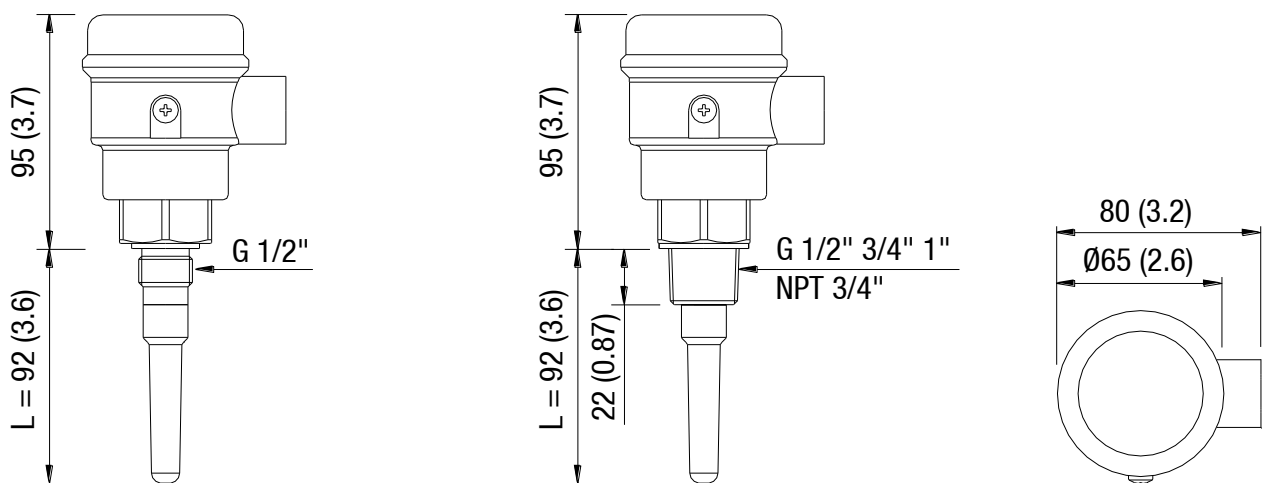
Abmessungen CN 7120, Gehäuse Ø 65 mm
